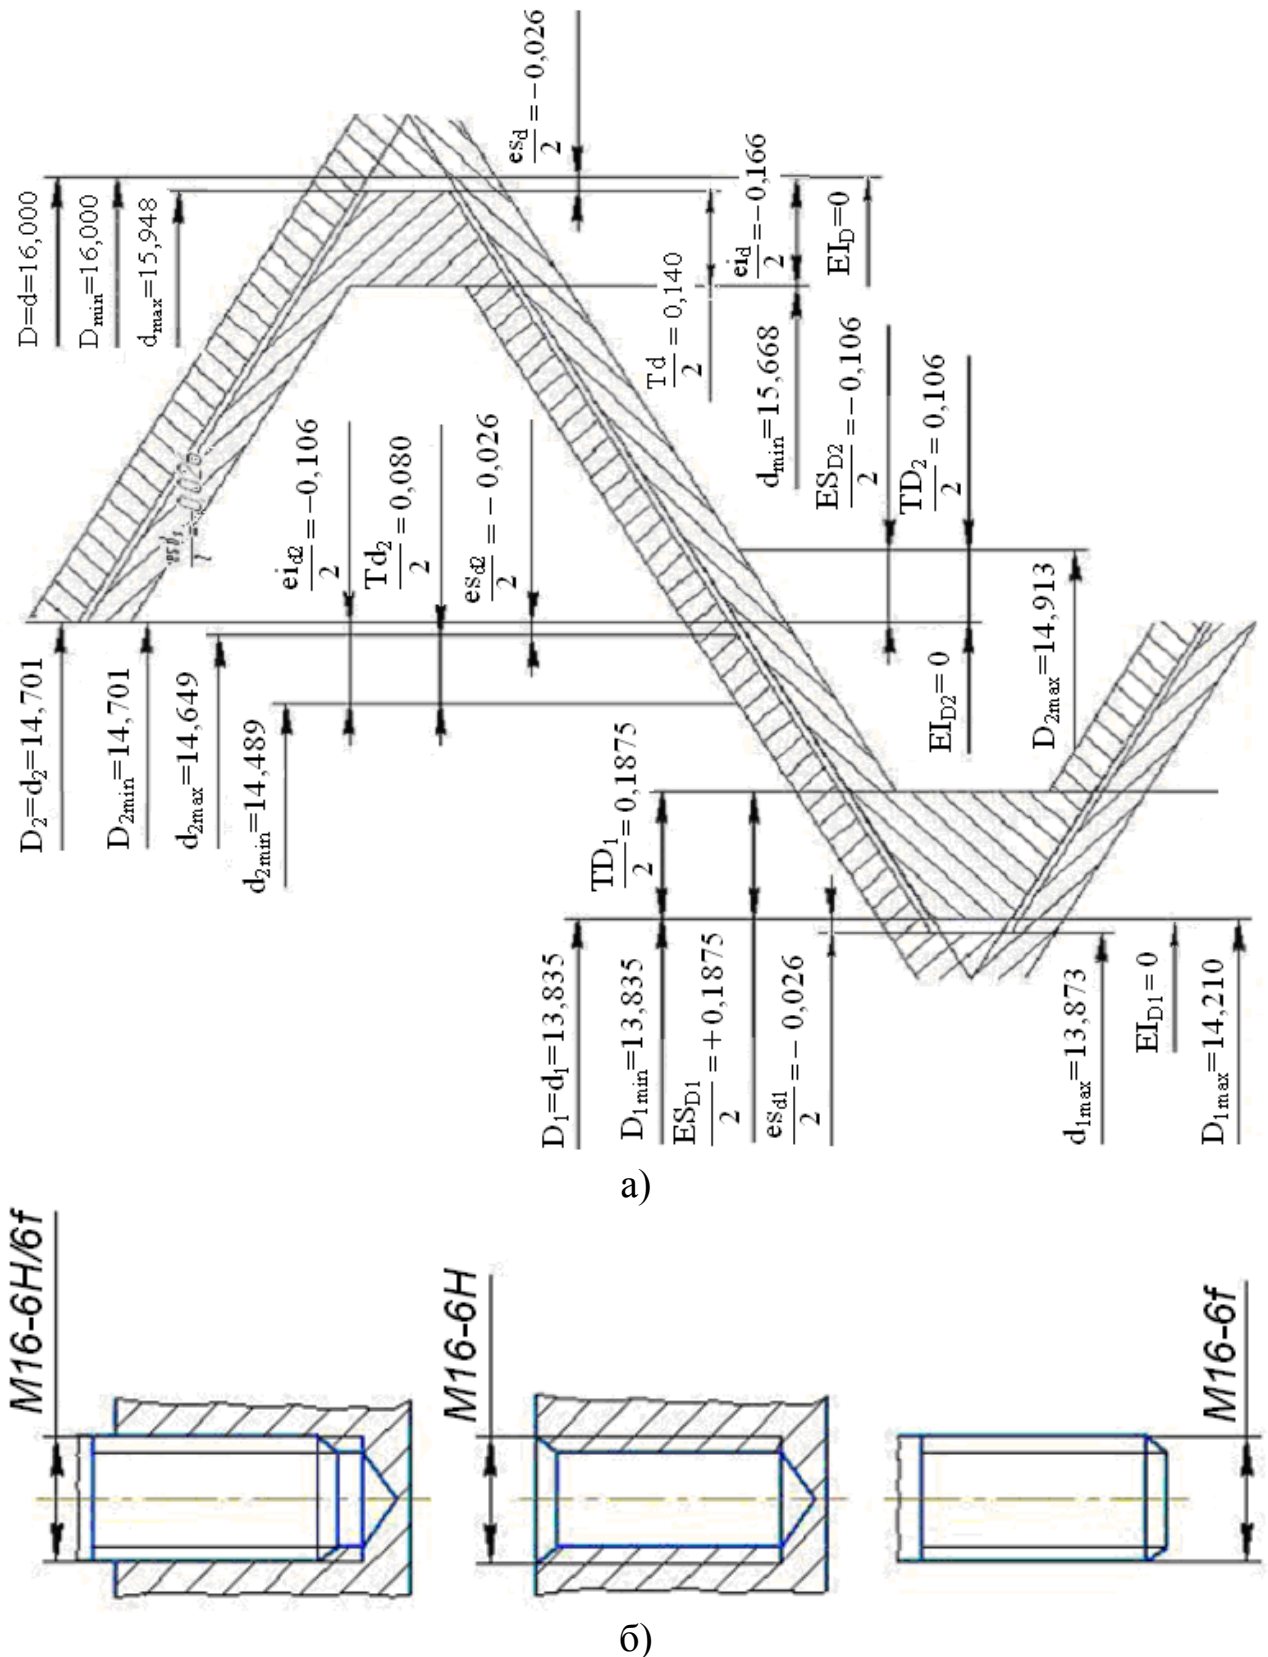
Схема розташування полів допусків (а), складальний та подетальні кресленики (б) нарізного з'єднання
